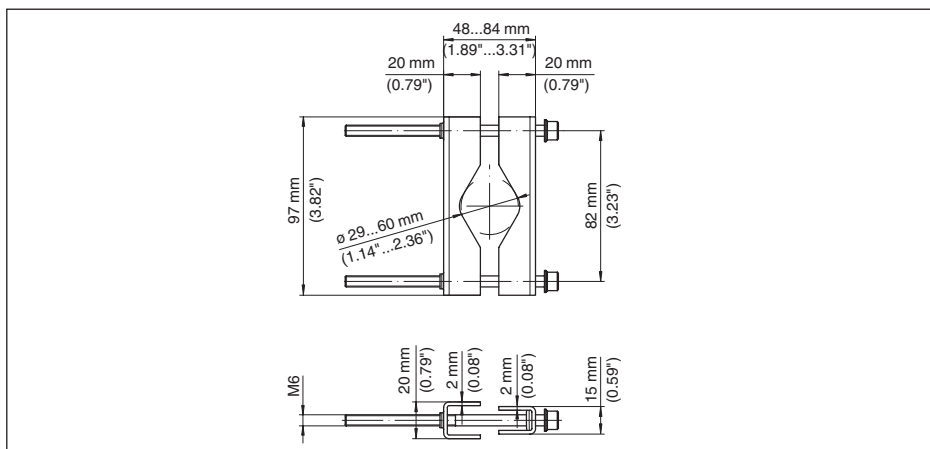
Suportes para montagem do VEGADIS 81 em tubo
